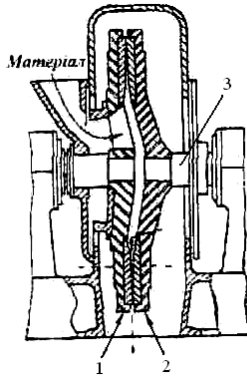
Схема дискової дробарки: 1, 2 – диски; 3 – горизонтальний вал
